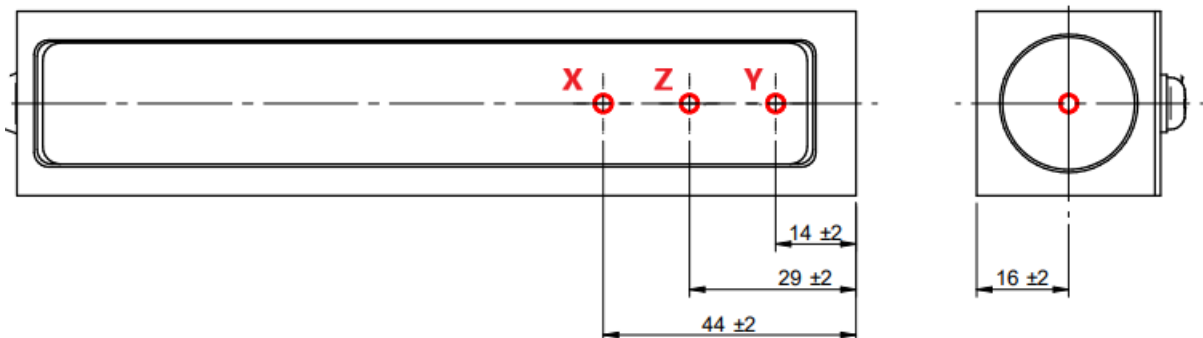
Posición (en mm) de cada sensor dentro del Magnetometer Mag03-MS1000 [23].
